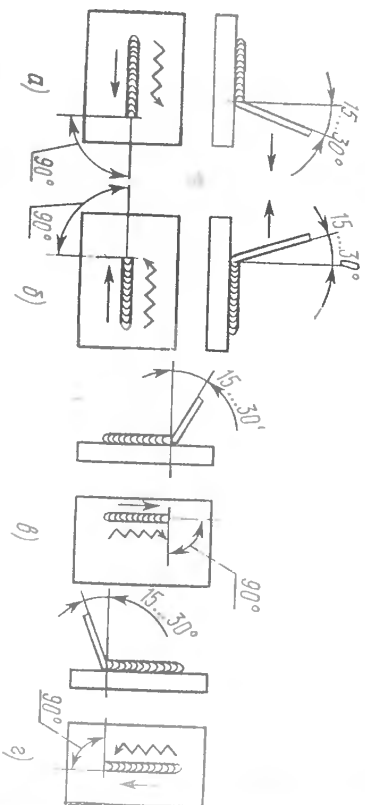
Направления сварки и углы наклона электрода:
